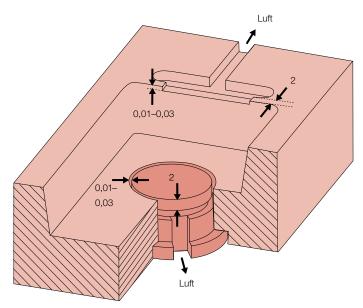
Werkzeugentlüftung (Maßangaben in mm)
